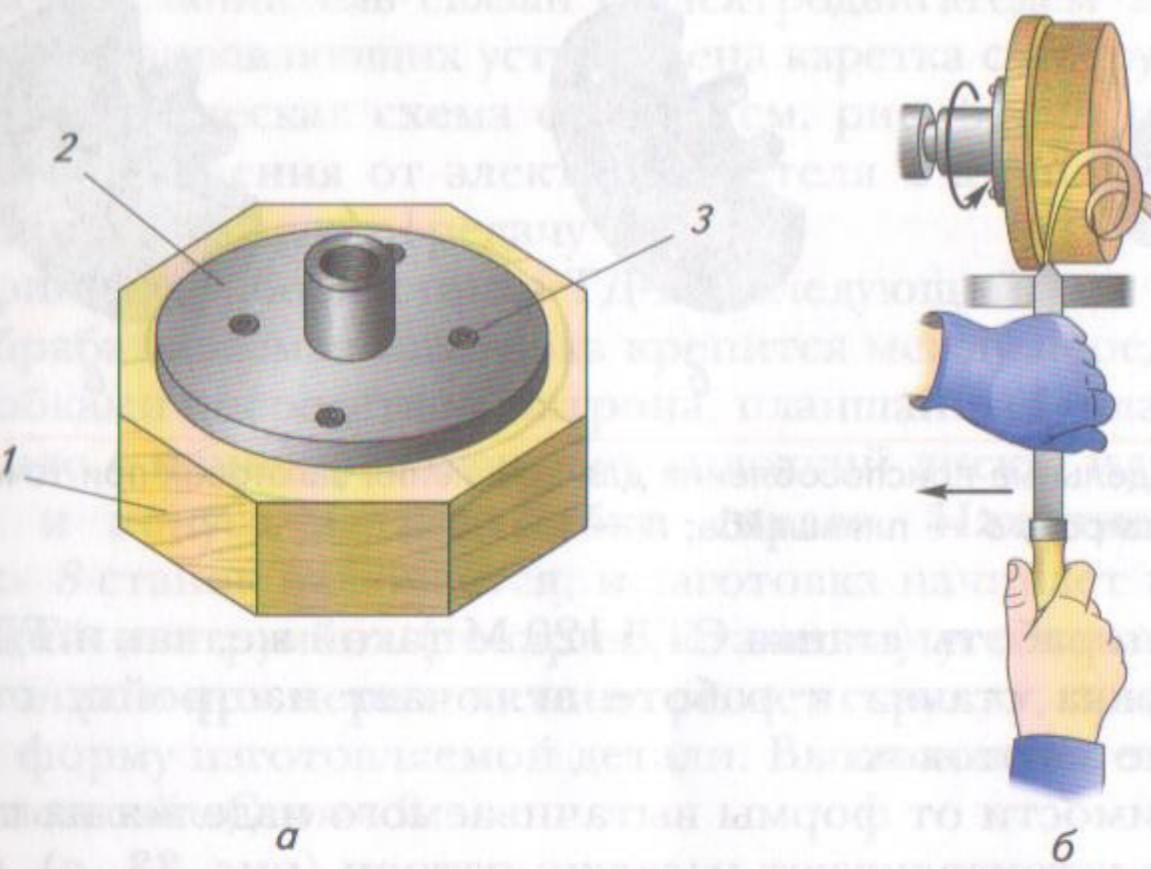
Крепление (а) и точение (б) заготовки на планшайбе: 1 — заготовка; 2 — планшайба; 3 — шуруп
